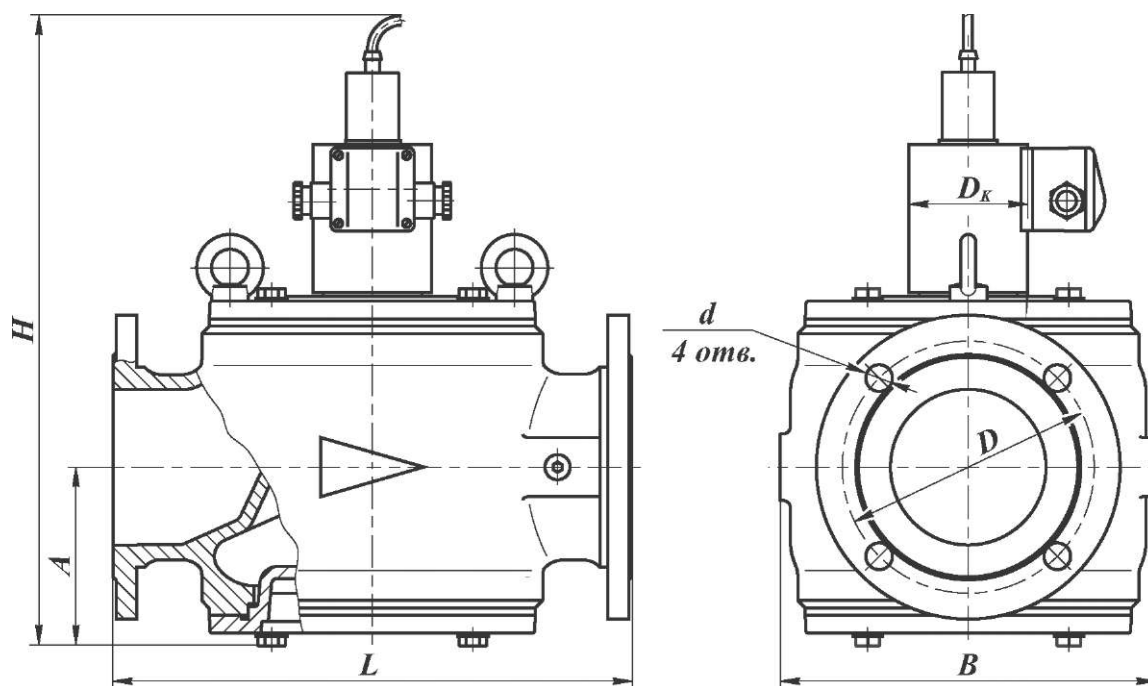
Клапаны на Ду40, 50, 65, 80, 100 фланцевые с датчиком положения в стальном корпусе
